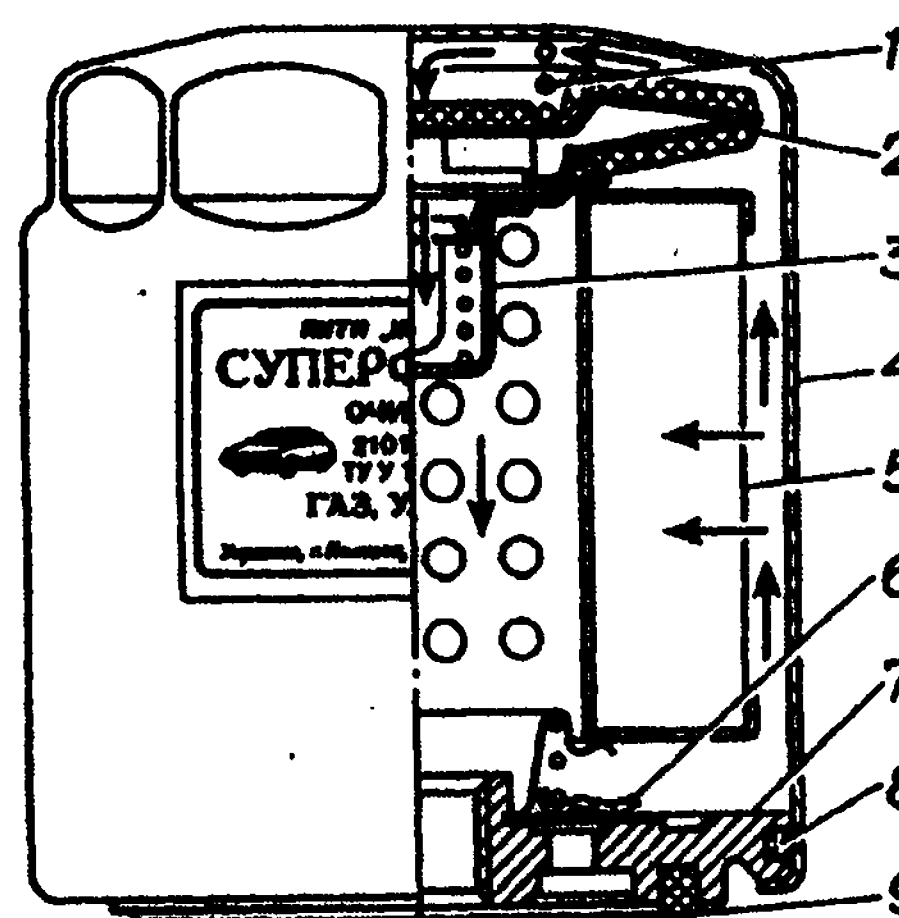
Масляный фильтр 2101С1012005-НК-2: 1 - пружина; 2 - фильтрующий элемент перепускного клапана; 3 - перепускной клапан; 4 - корпус; 5 - фильтрующий элемент; 6 - противодренажный клапан; 7 - стопорное кольцо; 8 - прокладка; 9 - крышка
